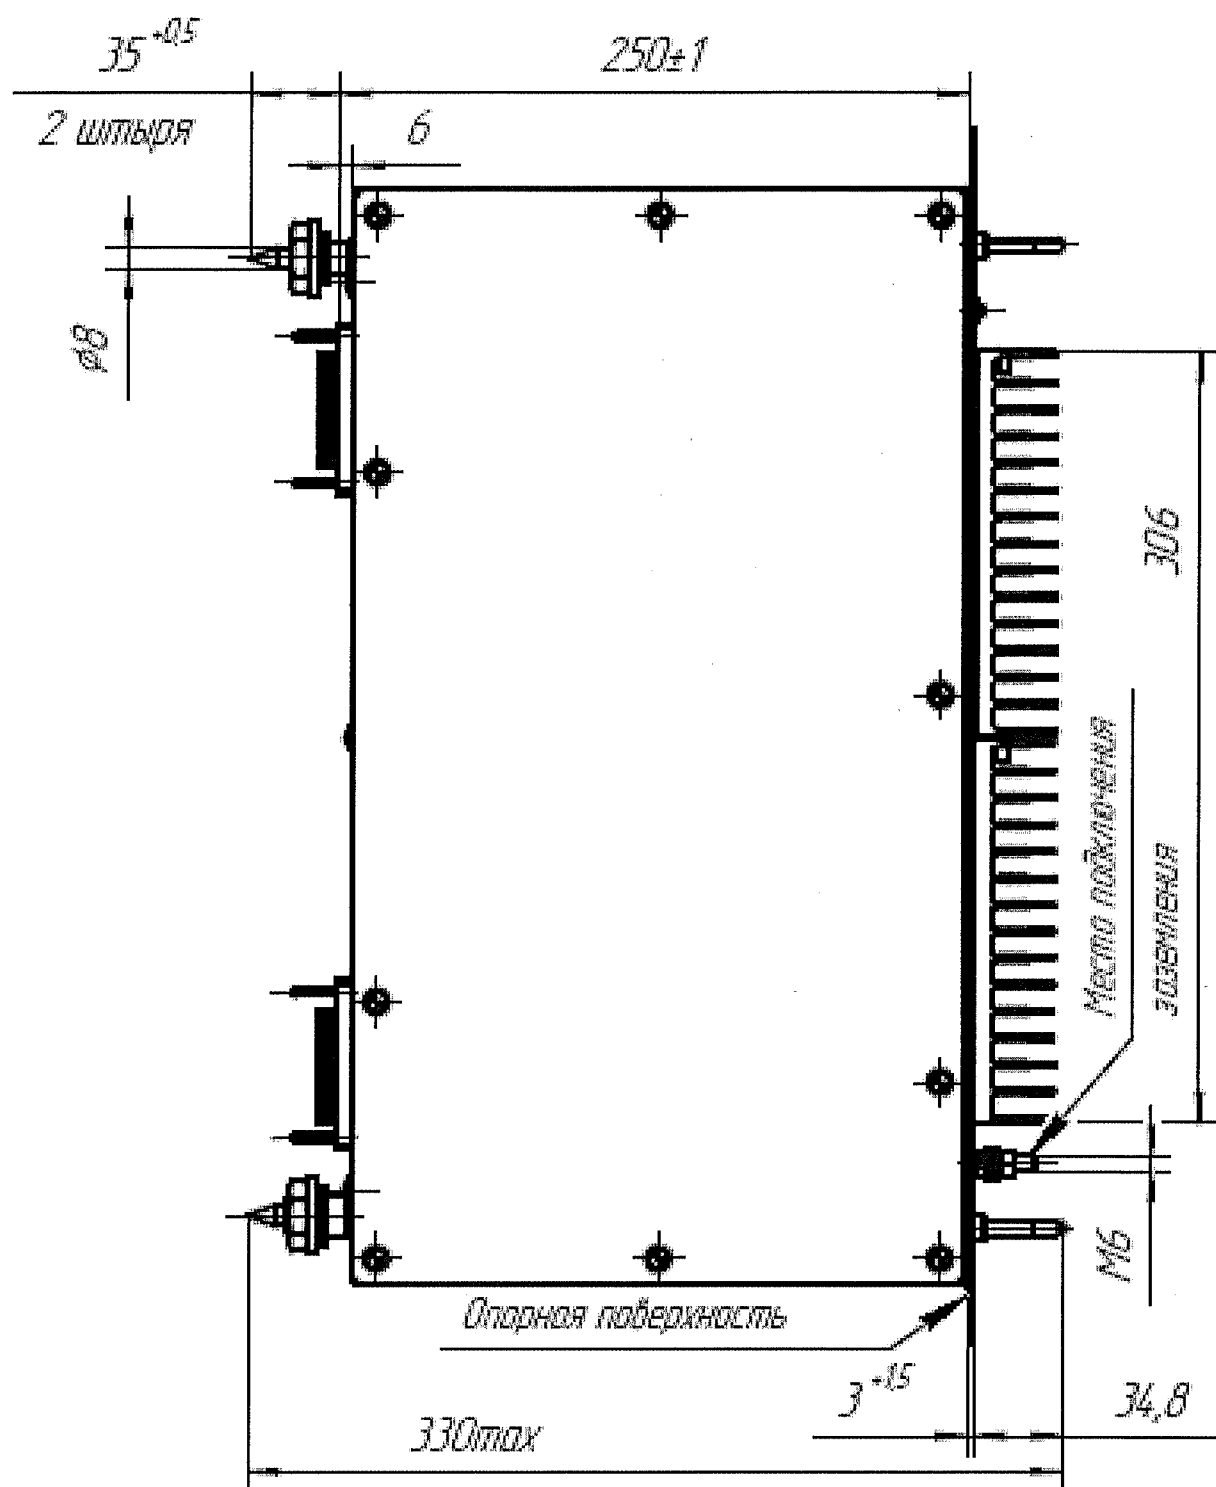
Вид снизу (развернуто, размеры для справки)
